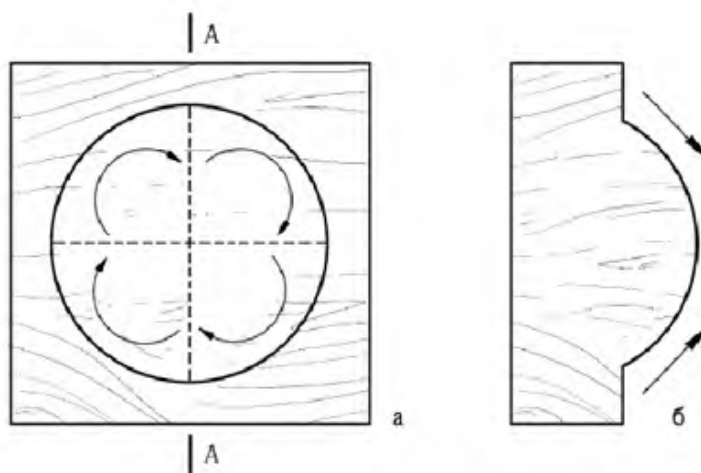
Выполнение выпуклой формы на торце заготовки (стрелками показано направление движения инструмента)
